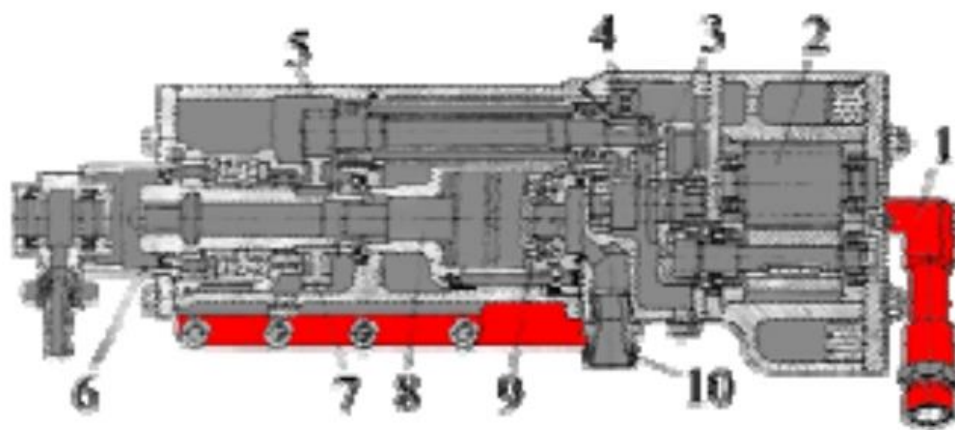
Розріз бурильної головки 1100-1-1М(БУ-1): 1 – патрубок; 2 – шестерний пневматичний двигун; 3, 4, 5, 7 – шестерні; 6 – букси; 8 – поршень-ударник; 9 – пневматичний ударник; 10 – патрубок
